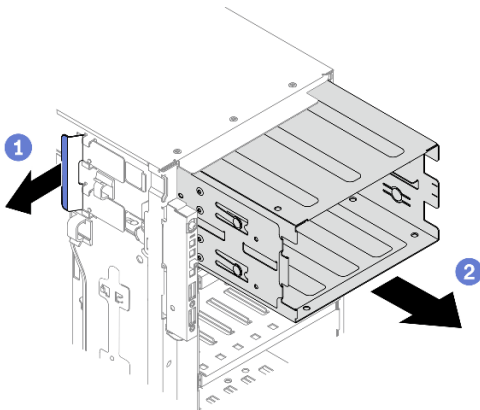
Entfernen der Halterung für optisches Laufwerk
